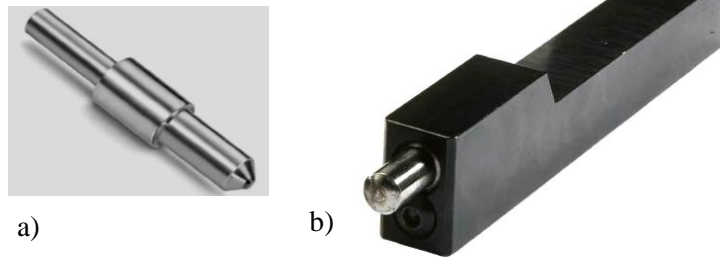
Outil du brunissage .commercialisé par la firme *COGSDILL TOOL*:
